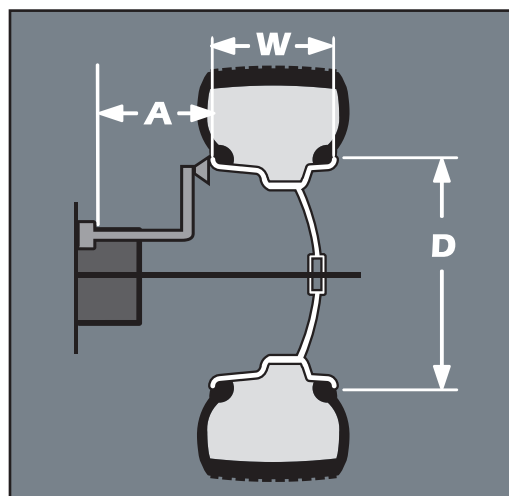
Dimensions des pneus A, W et D (écart, largeur et diamètre)
